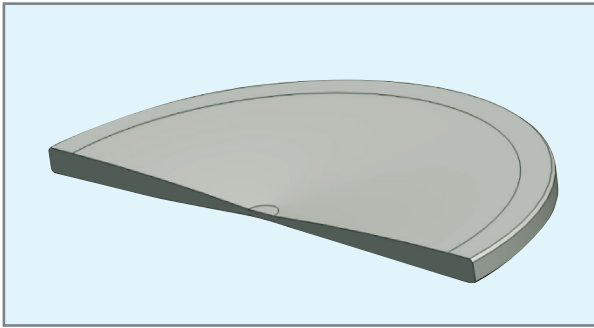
Vue en coupe d'une éprouvette FABIME2.
